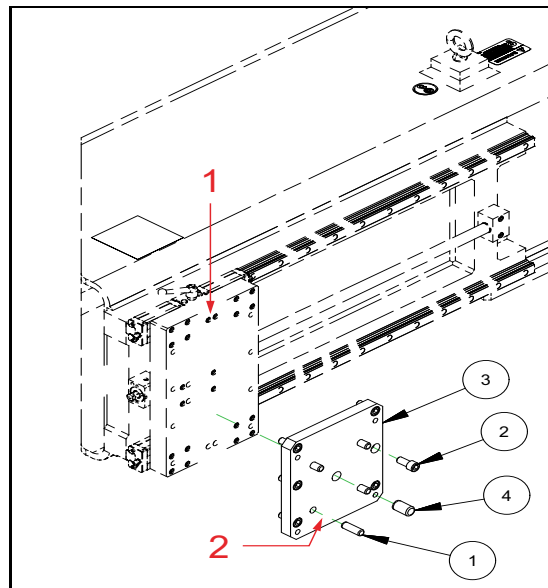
PLAQUE À GLISSIÈRE LATÉRALE
